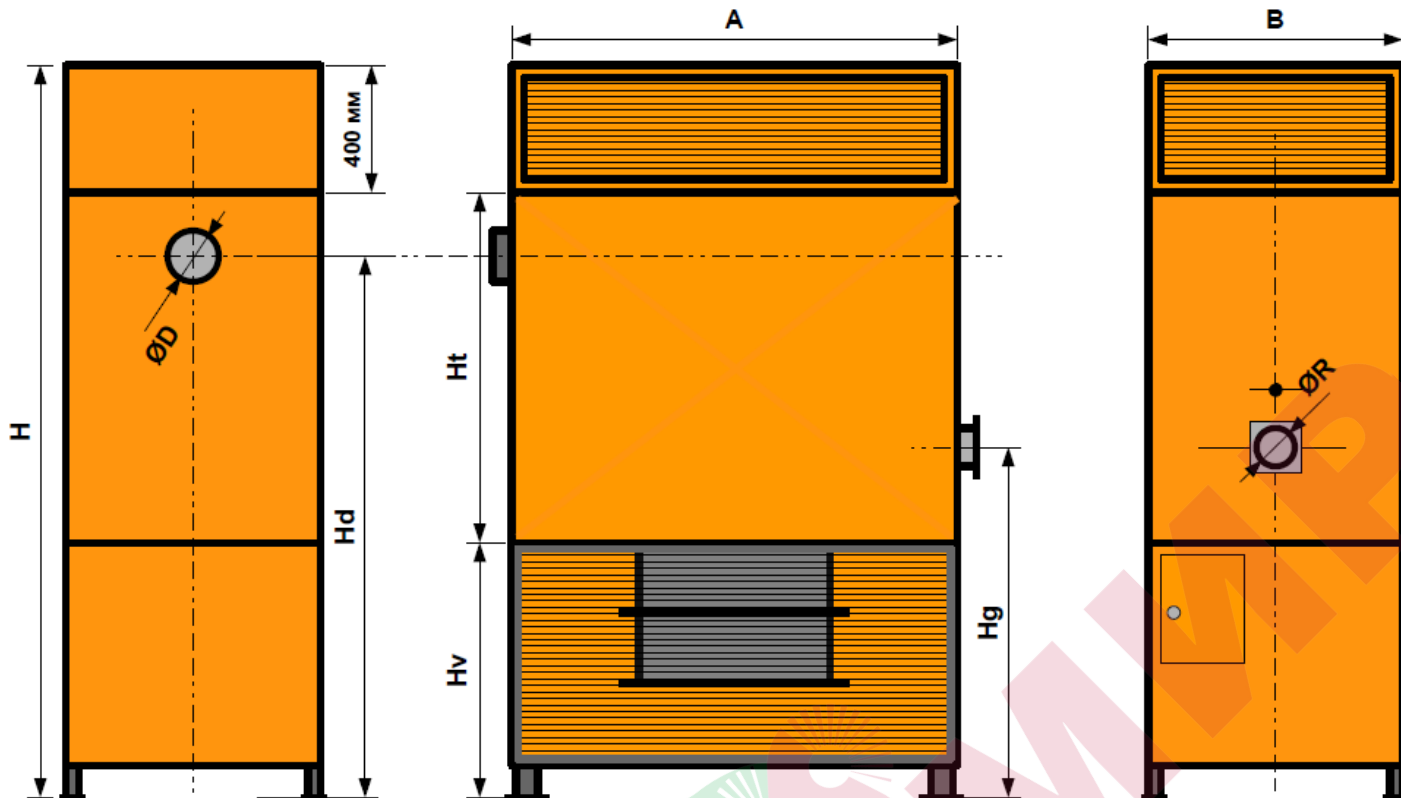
Габаритные размеры воздухонагревателей серии VT-P
